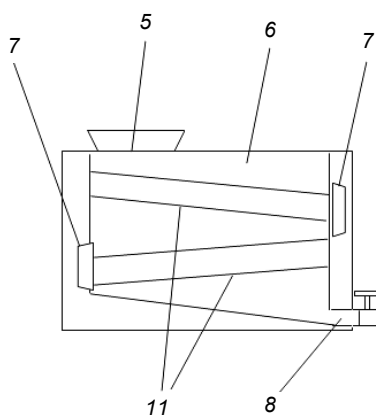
Снегоплавильная камера с газовыми горелками и газоходами
